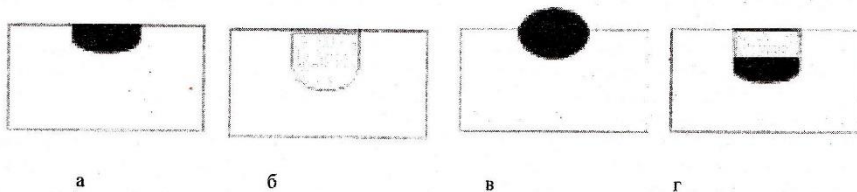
Типы воздействия лазерного излучения на поверхность обрабатываемого материала: а – поверхностный контраст, б – гравировка поверхности удалением материала, в – оплавление поверхности, г – гравировка с оплавлением
